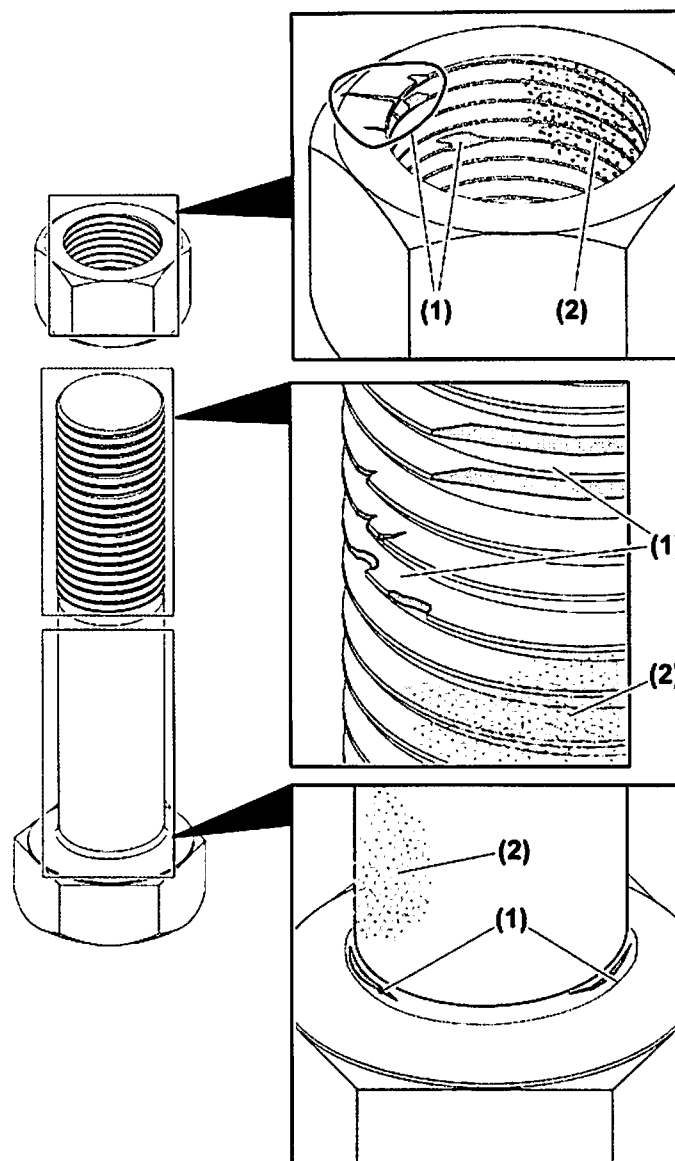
HV-Schraubverbindung auf Beschädigung und Korrosion prüfen
